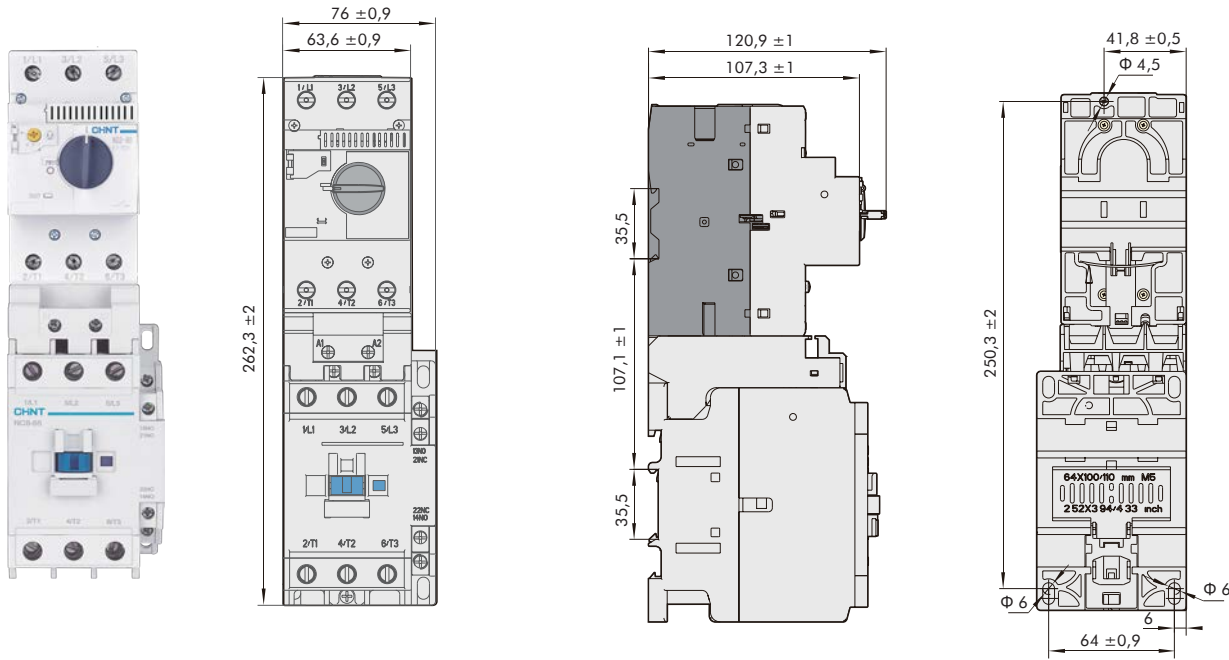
Vue d'ensemble et dimensions d'installation du CC-3(NS2) après assemblage avec le disjoncteur et le contacteur
